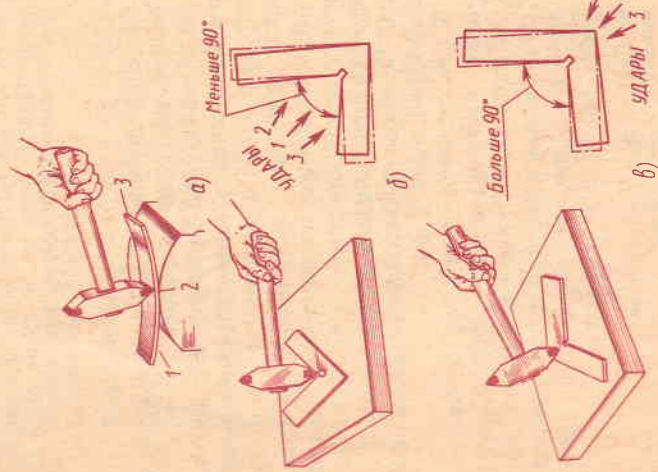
Правка (рихтовка) деталей из закаленного металла:
